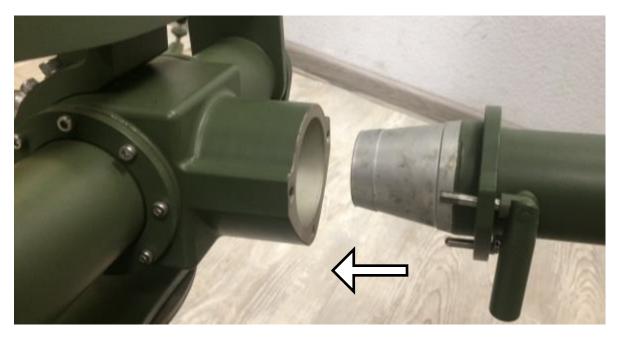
Установка держателя облучателя на опорную платформу
